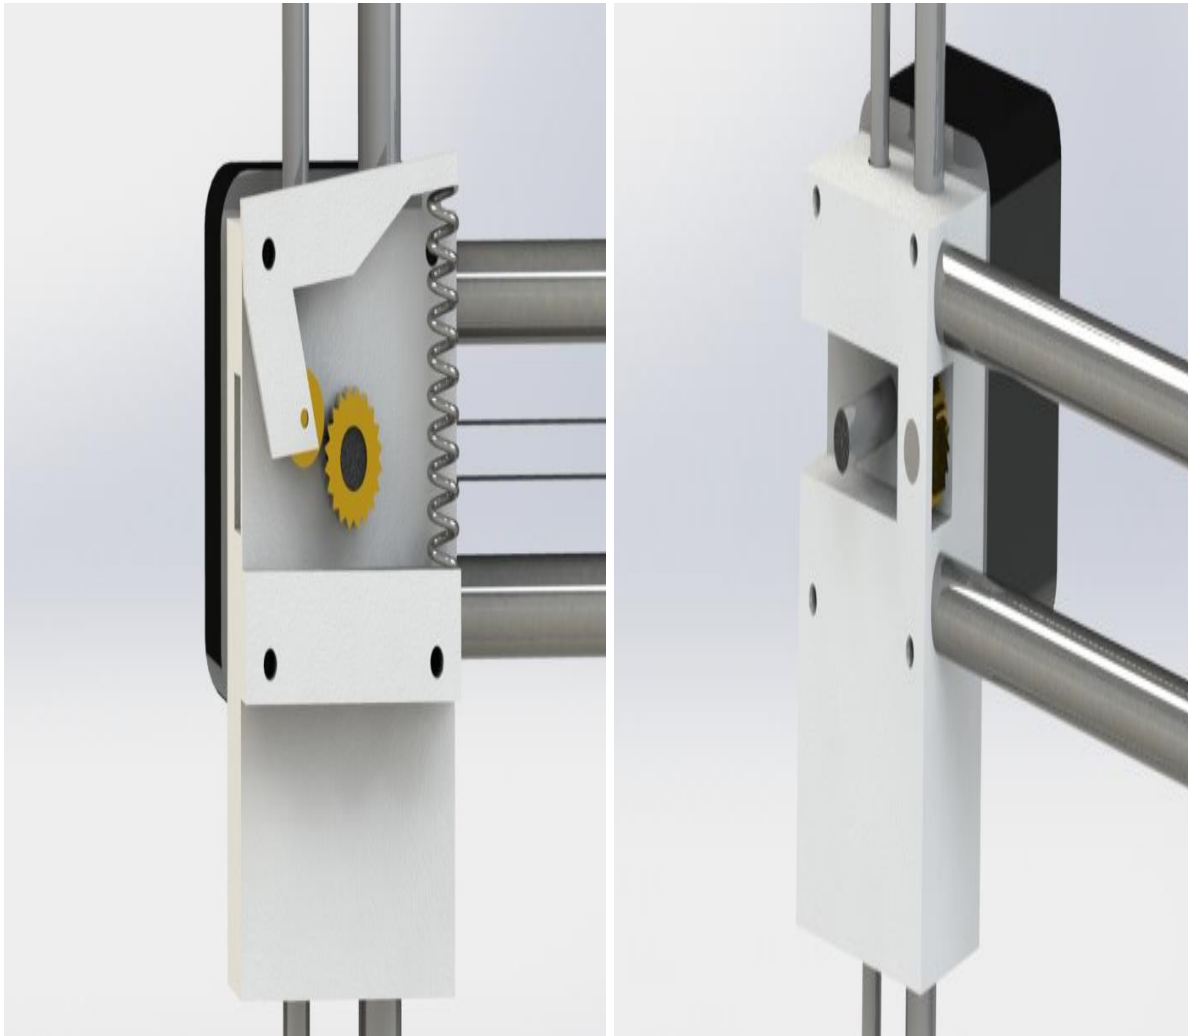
Detalle soporte eje X lado bowden con el conjunto del extrusor y detalle soporte eje X lado bowden sin el conjunto del extrusor
